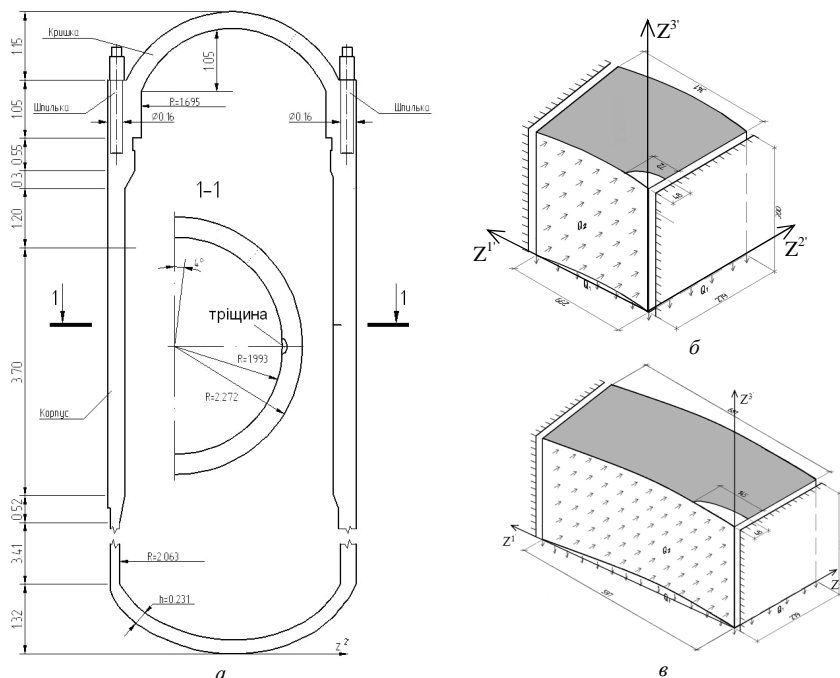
Схема корпусу реактора (а), розрахункові схеми для тріщин 0.67(б) та 0.33(е)
